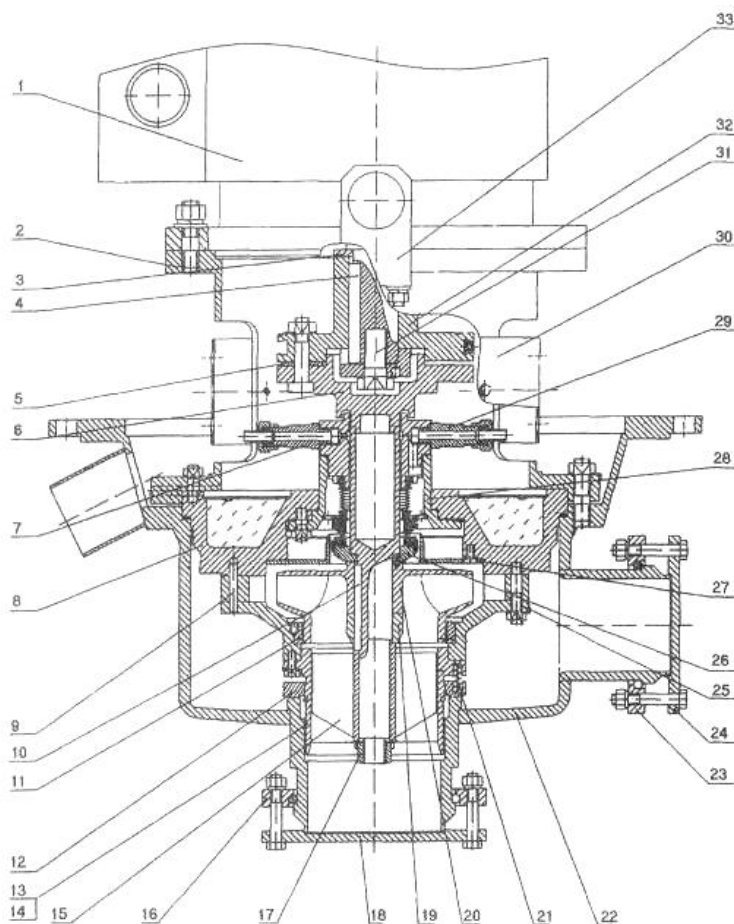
Конструкция вертикального моноблочного центробежного насоса типа НкпМ с корпусом под засыпную изоляцию:
